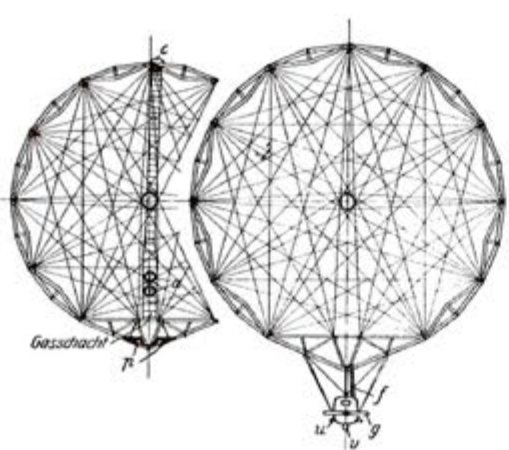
Querschnitt am Haupttring hinter der hinteren Maschinengondel.
